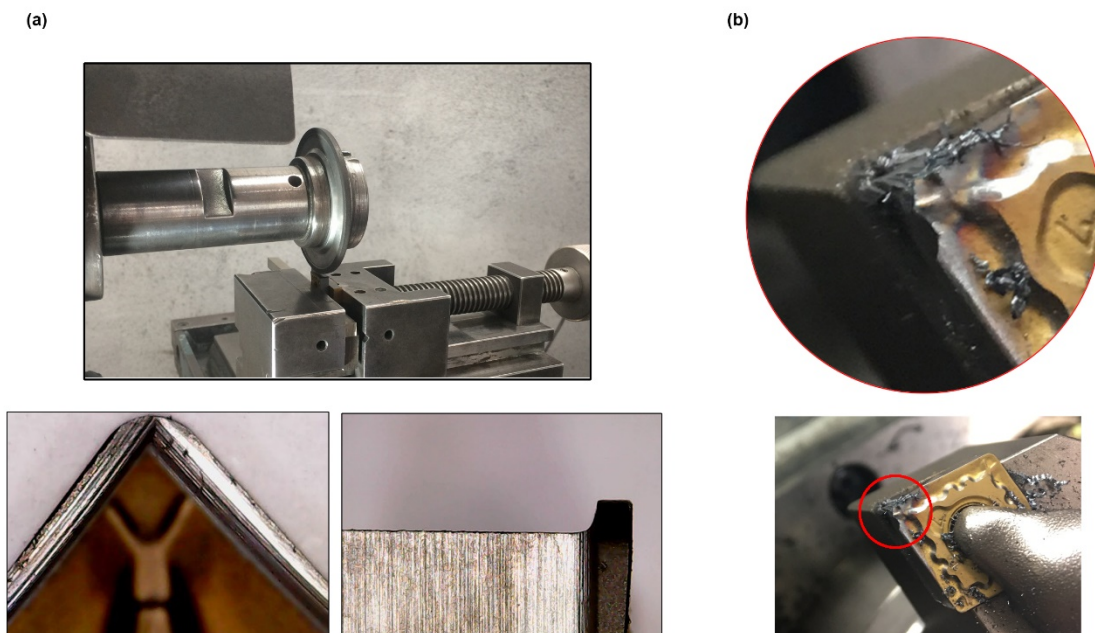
(a) Processo de fabricação do inserto protótipo. (b) Inserto segundos após contato com a peça a ser usinada.
